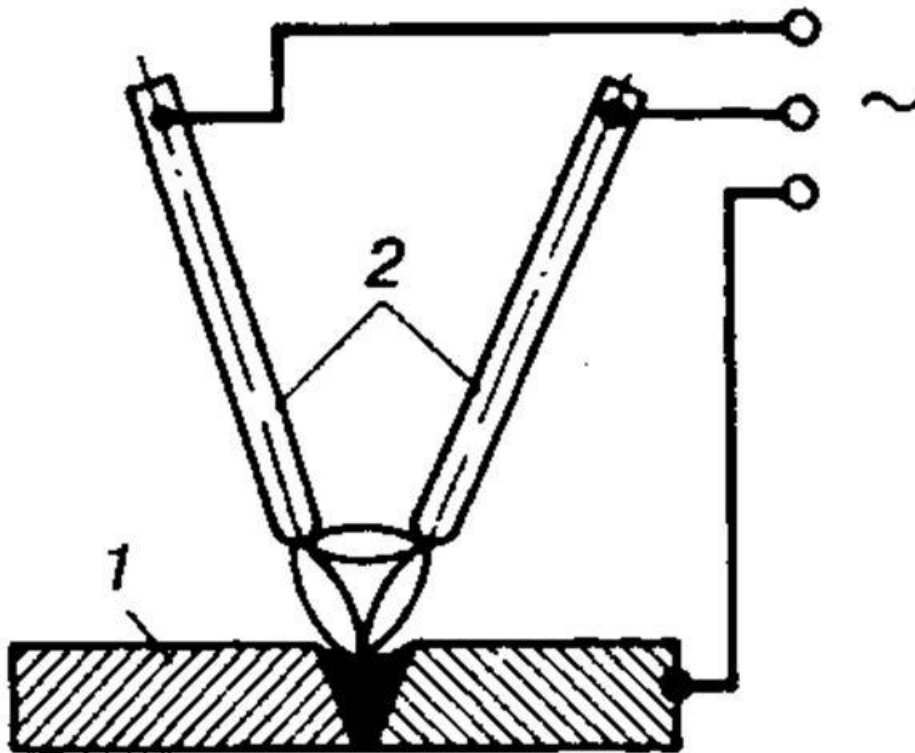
Схема дугового зварювання плавкими металевими електродами з використанням трифазної дуги
